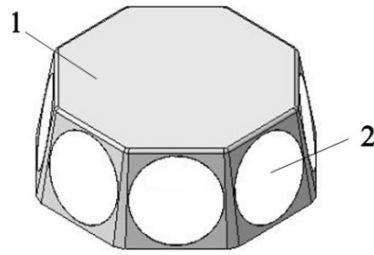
Світлоповертальний елемент: 1 – корпус; 2 – мікропризмний елемент
